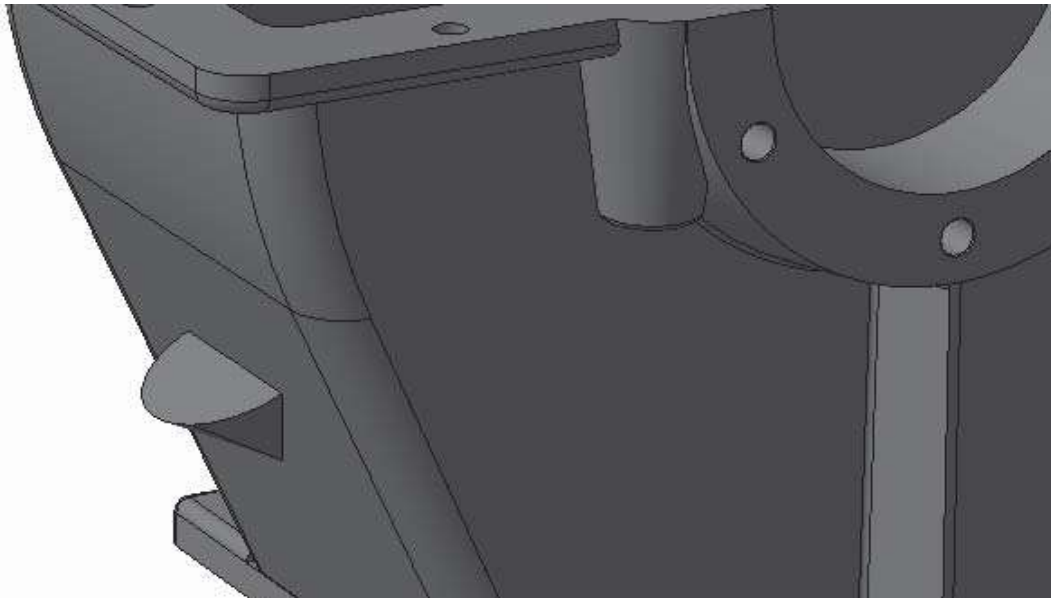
Початок формування ніші в корпусі під масловказівний покажчик
